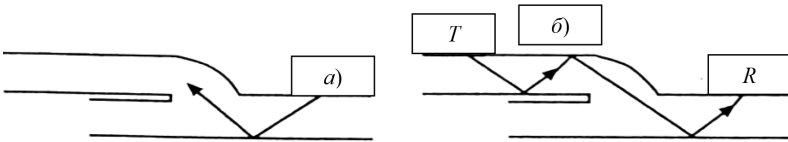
Схемы прозвучивания нахлесточных сварных соединений: а – отраженными лучами преобразователя; б – раздельно-совмещенная схема
